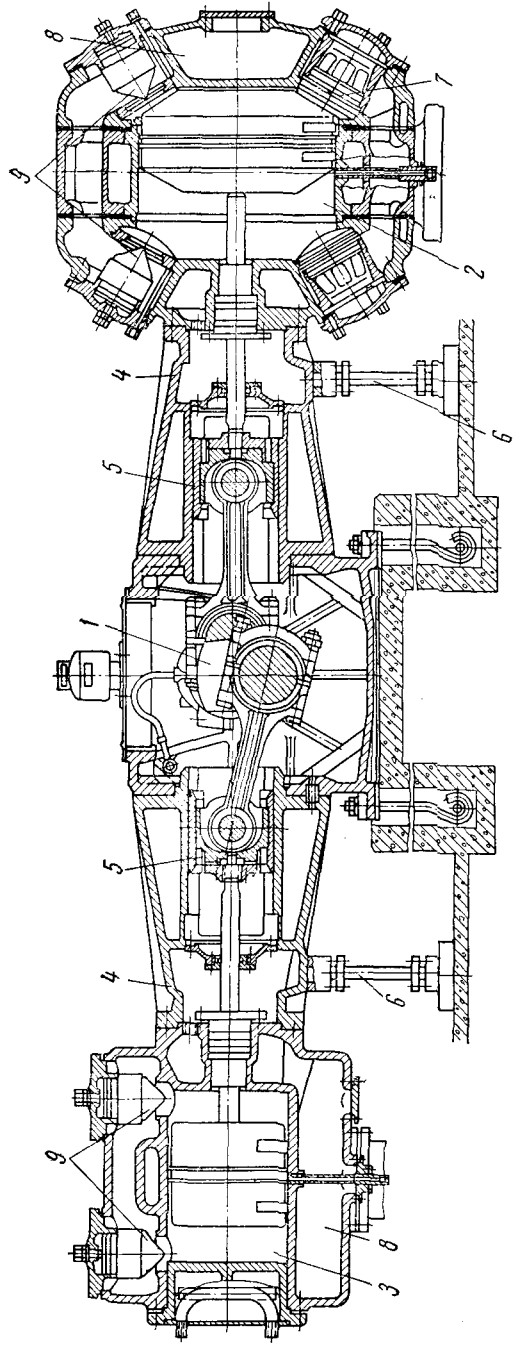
Разрез по цилиндрам компрессора 4М10-100/8
